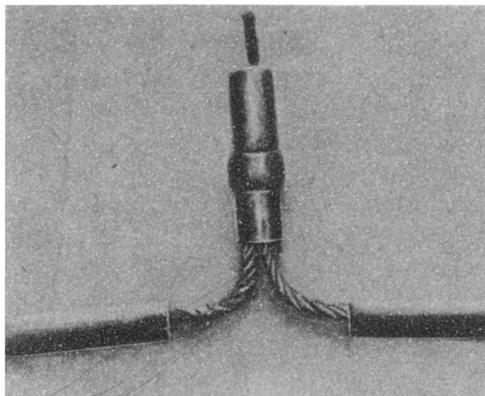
Образец контактного соединения проводов марки ПСРП с алюминиевыми жилами кабеля
